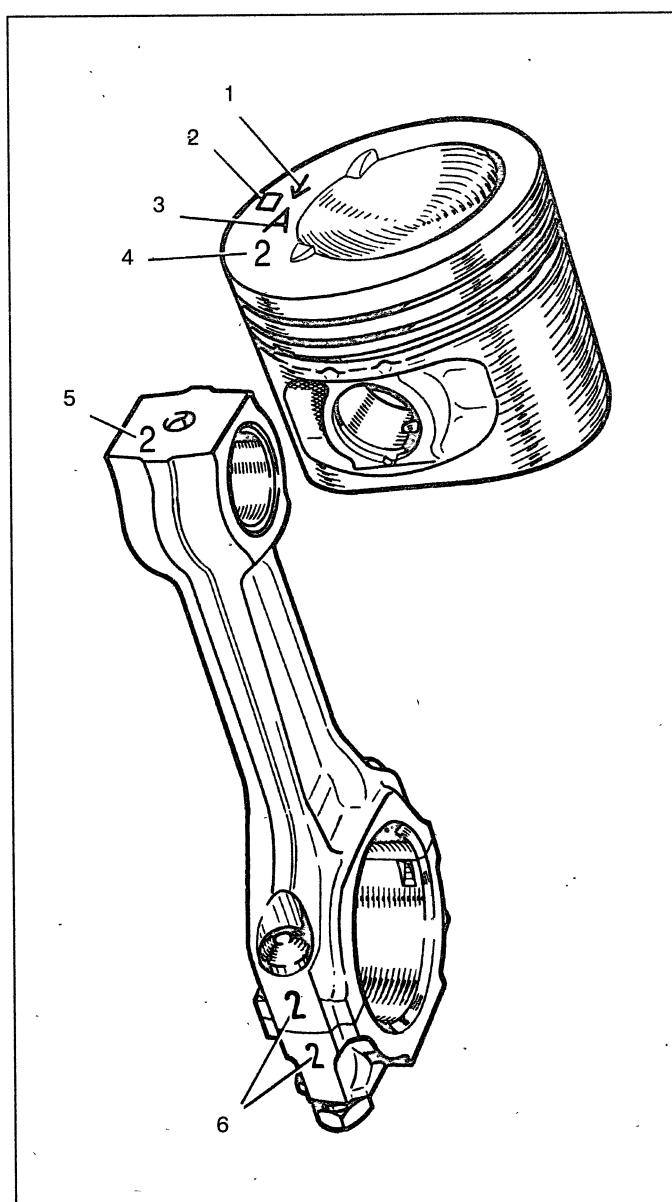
Маркировка поршня и шатуна: 1 – стрелка для ориентирования поршня в цилиндре; 2 – ремонтный размер; 3 – класс поршня; 4 – класс отверстия для поршневого пальца; 5 – класс шатуна по отверстию для поршневого пальца; 6 – номер цилиндра
